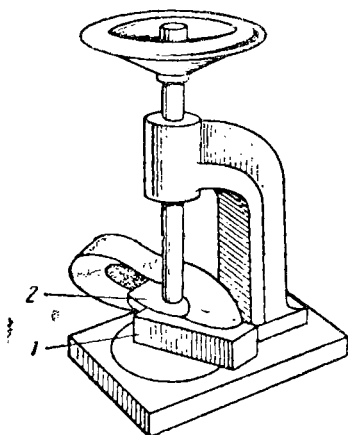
Запрессовка пучков галош в цельнолитой пресс-форме:
